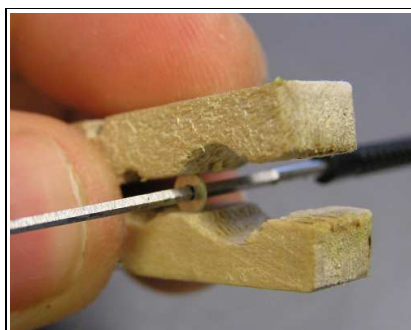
Mit Hilfe der Holzklammer das Loch auf 1,4mm aufreiben.
